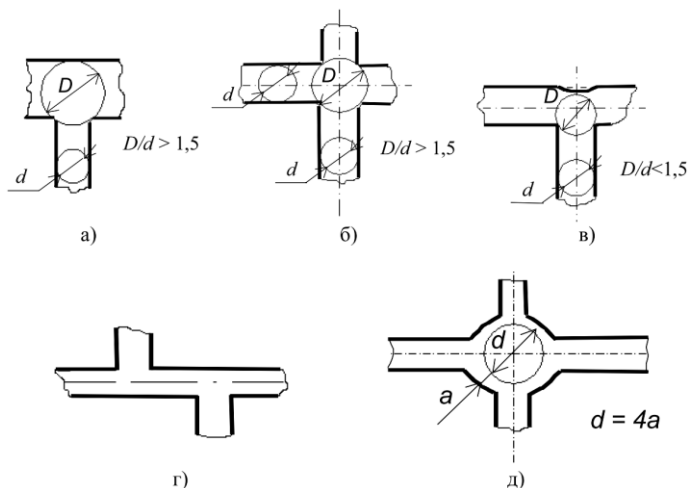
Устранение местного скопления металла в стенках отливки
